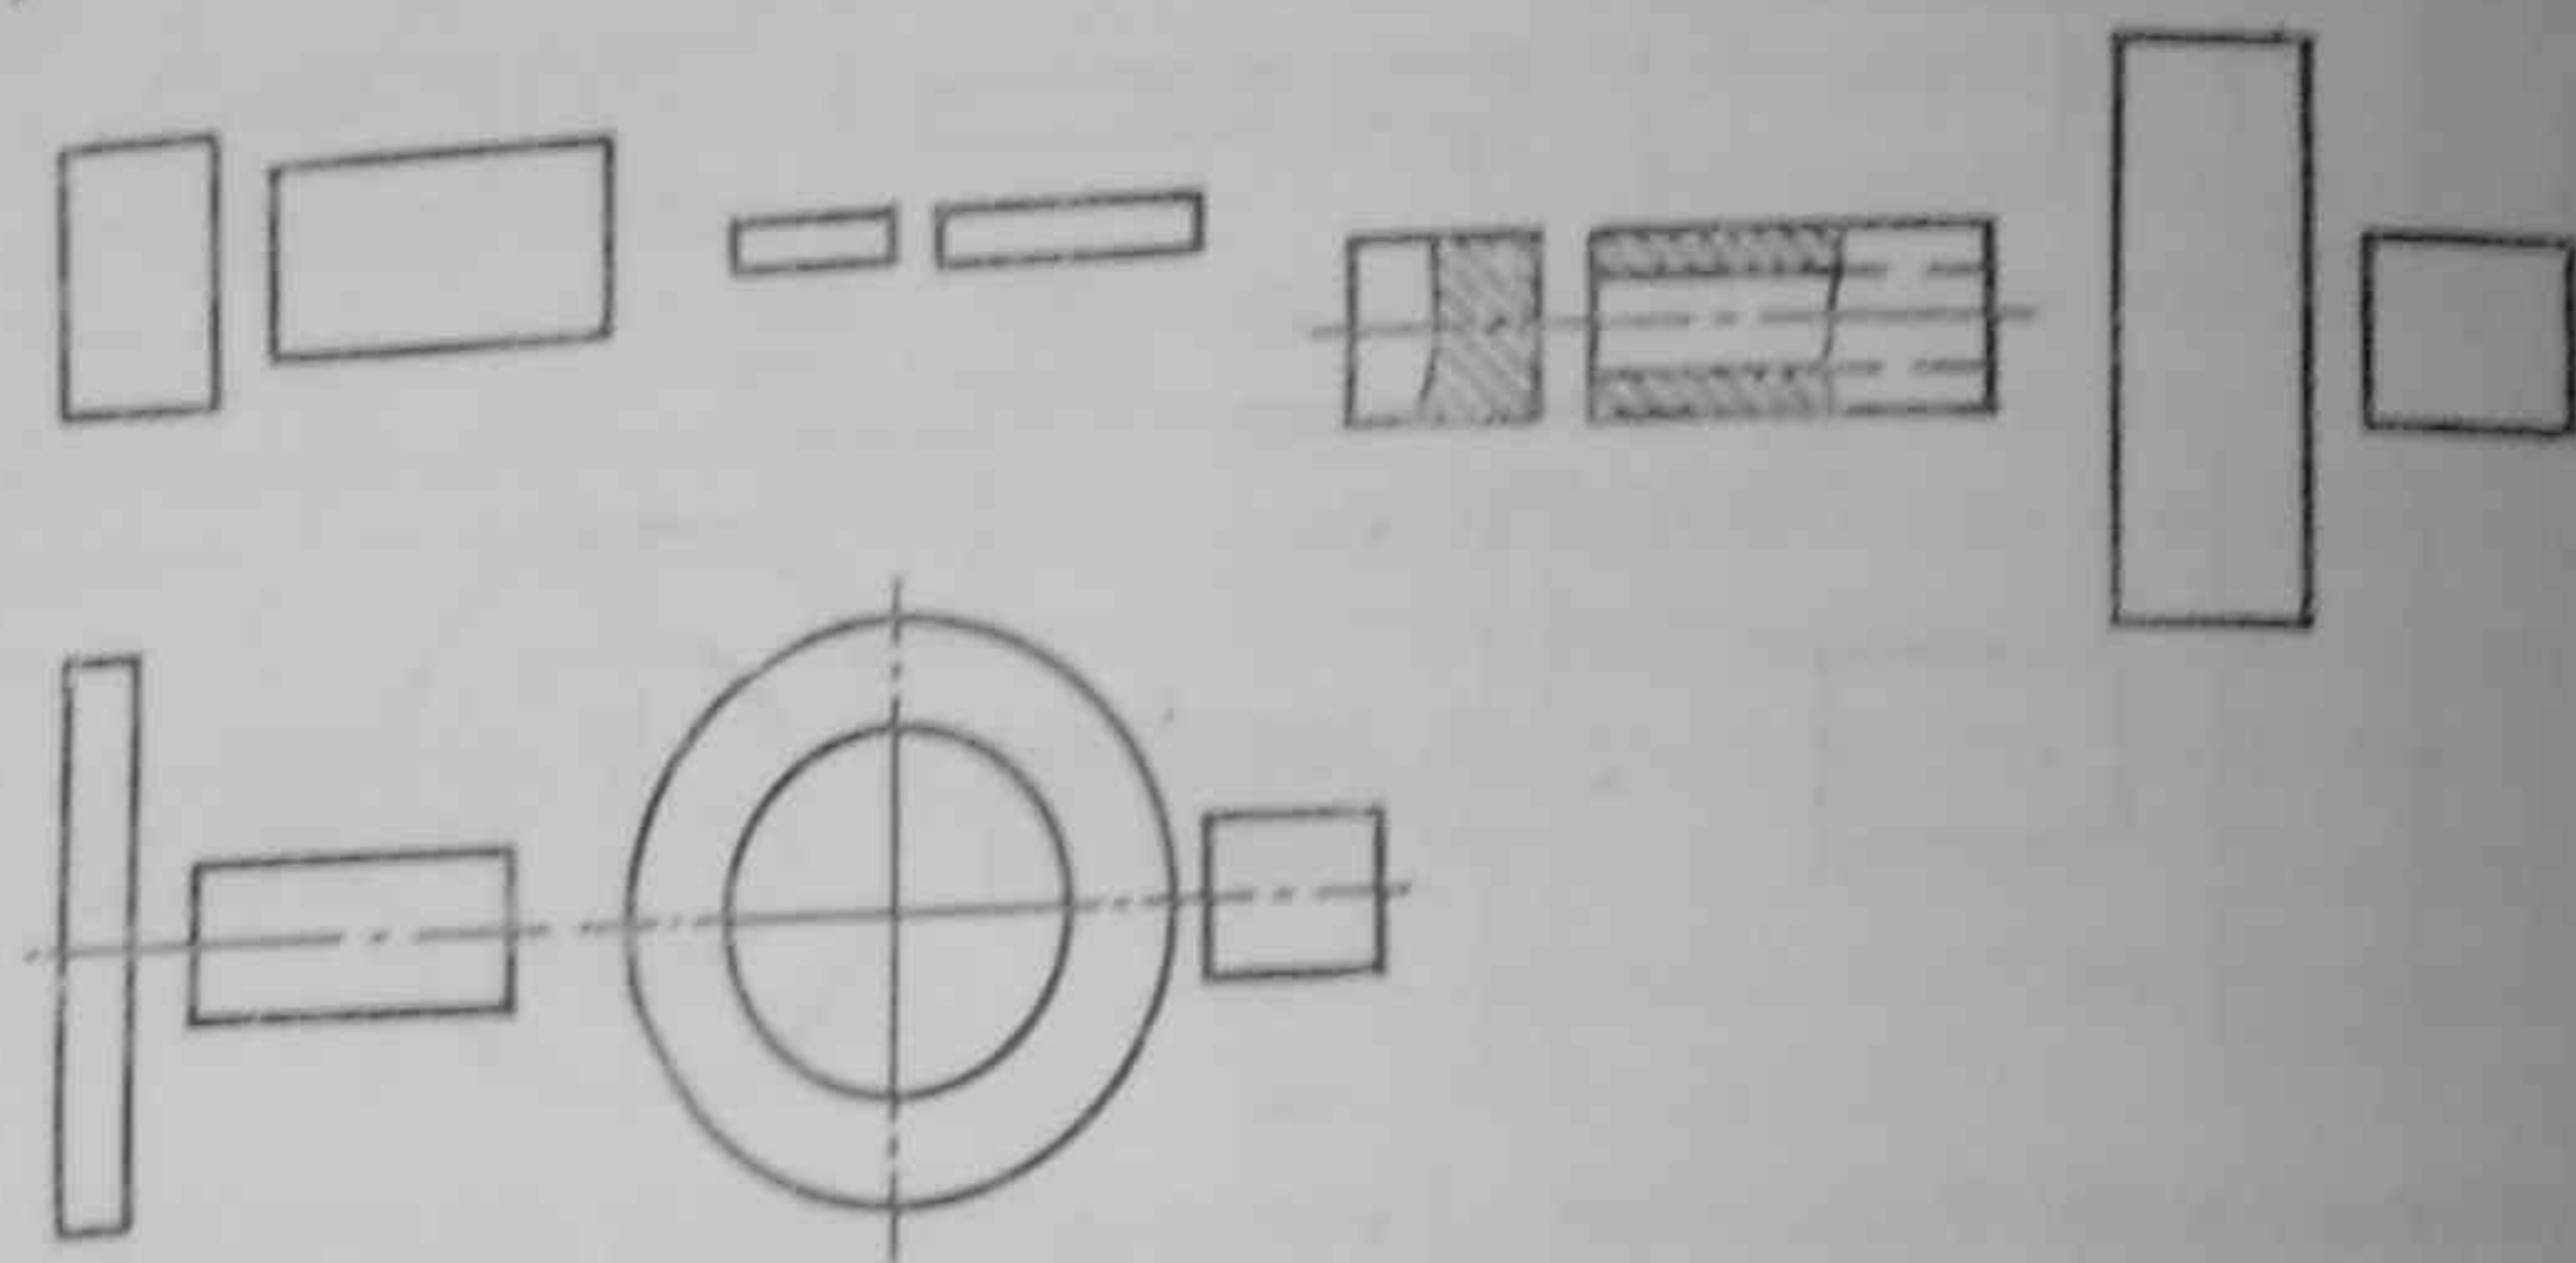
Типы сварных соединений стыковой сварки оплавлением
